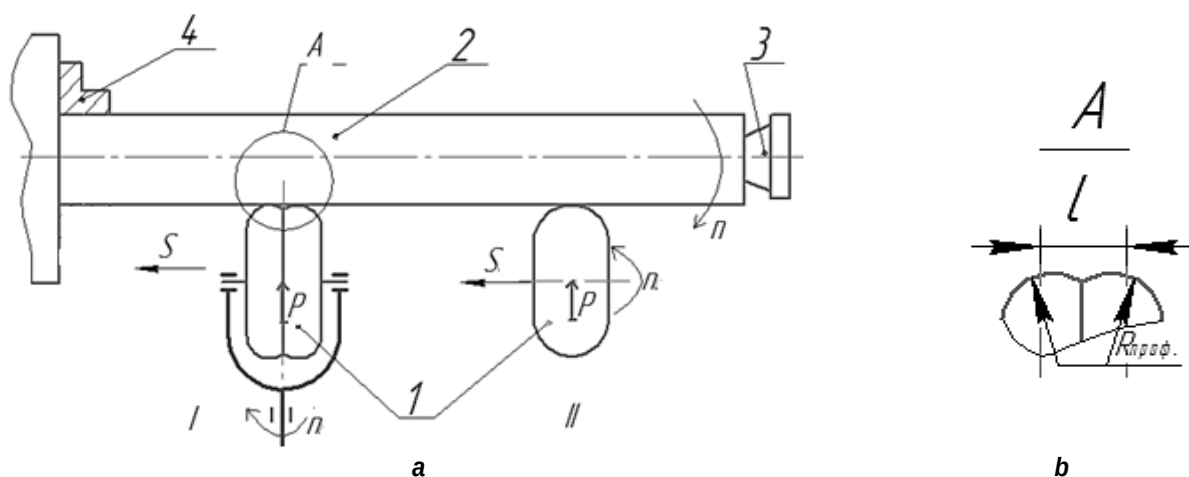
А – схемы упрочняющей обработки двухрадиусным (I) и однорадиусным роликом (II) на токарном станке; б – вид рабочей части двухрадиусного ролика:
